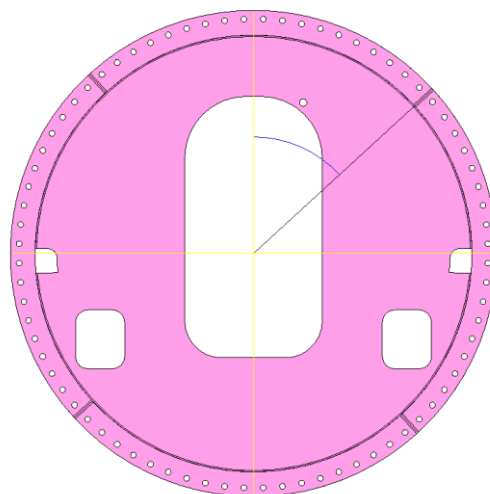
Zkosení vnitřního plechu a místo svaru
